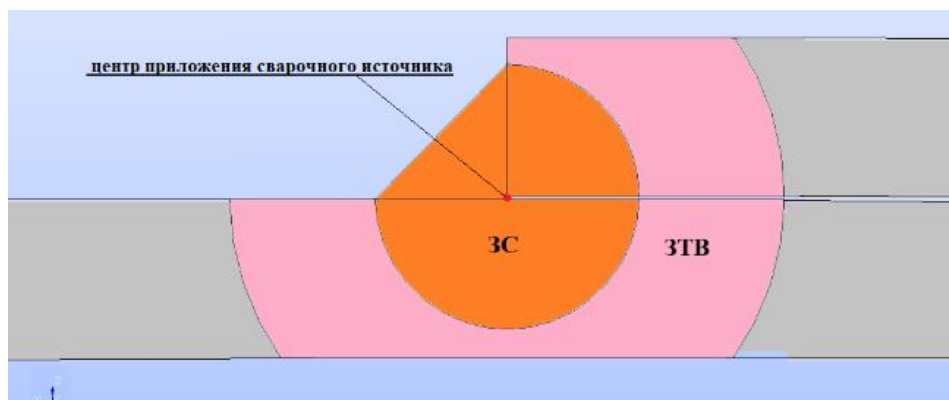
Геометрия ЗТВ и ЗС нахлесточного сварного соединения
